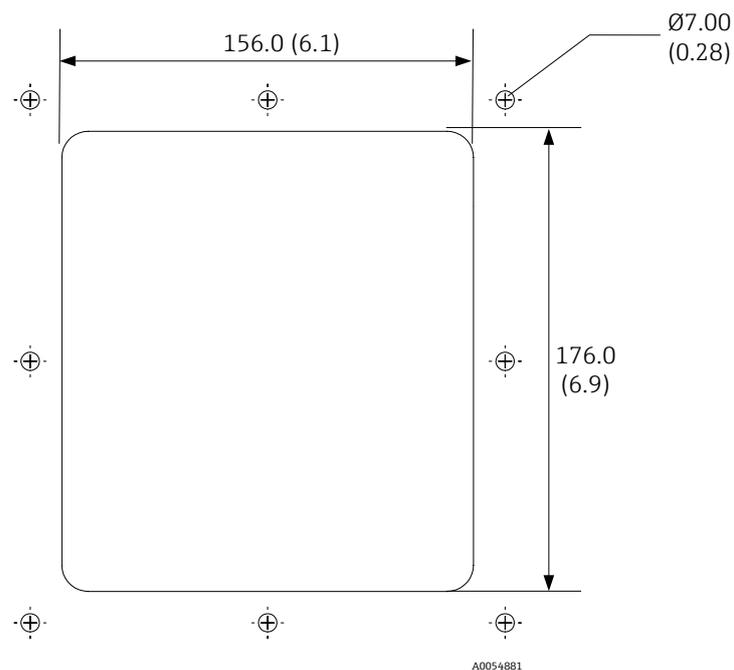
Découpe de montage du boîtier. Dimensions : mm (in)
